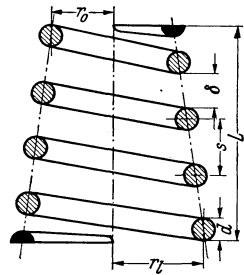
Kegelstumpffeder mit Kreisquerschnitt.
